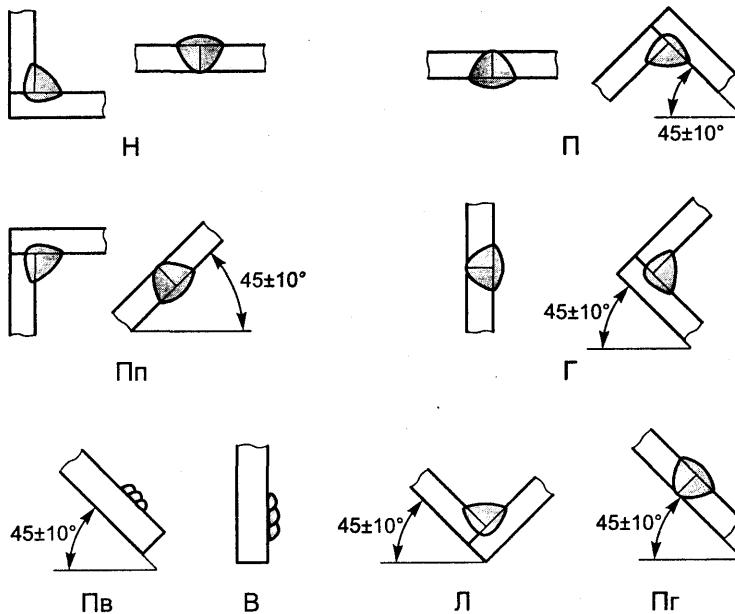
Обозначение сварных швов по их положению в пространстве:
